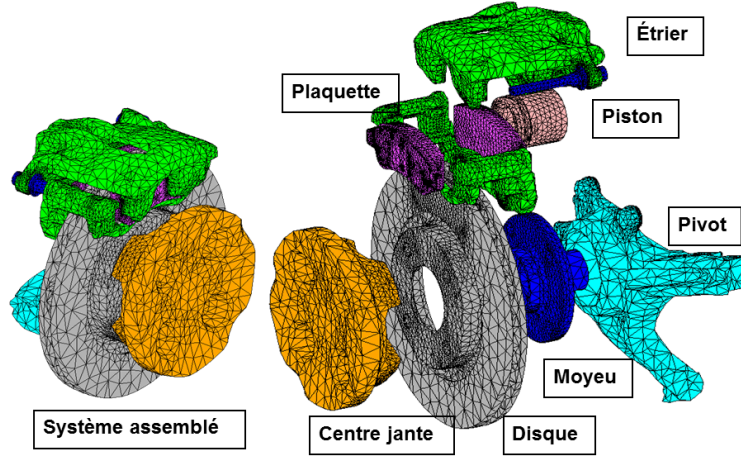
Modèle éléments finis étudié - vue assemblée (à gauche) et vue éclatée (à droite)
